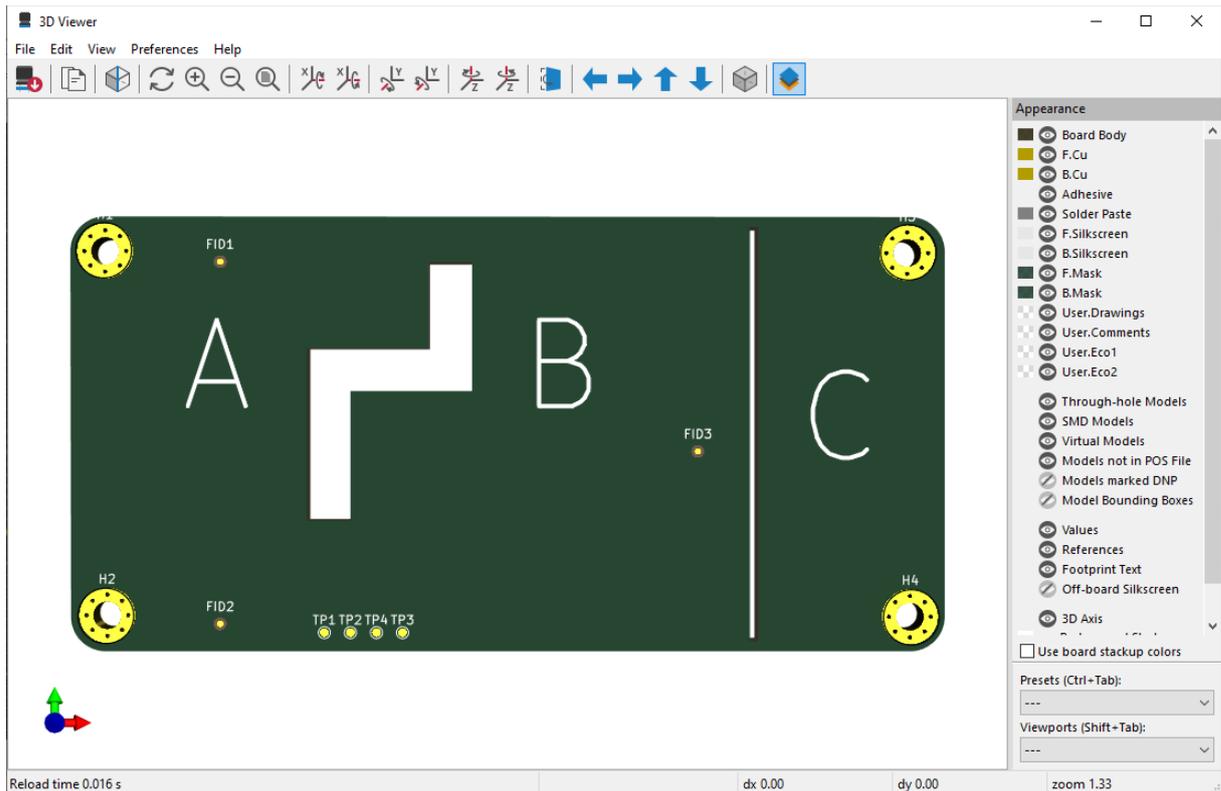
Modello 3D del PCB con l'aggiunta dei test points.
